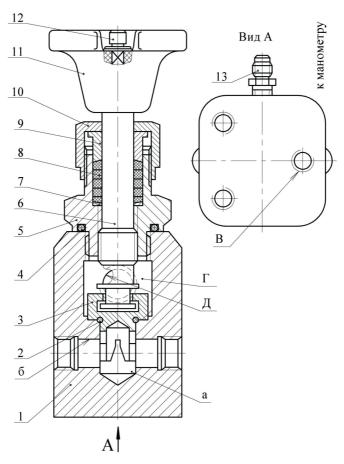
Вентиль регулирующий: 1 – корпус; 2, 4 – резиновое кольцо; 3 – клапан; 5 – корпус штока; 6 – шток; 7 – шайба; 8 – плетеная набивка; 9 – упор; 10 – гайка; 11 – маховик; 12 – винт; 13 – штуцер
